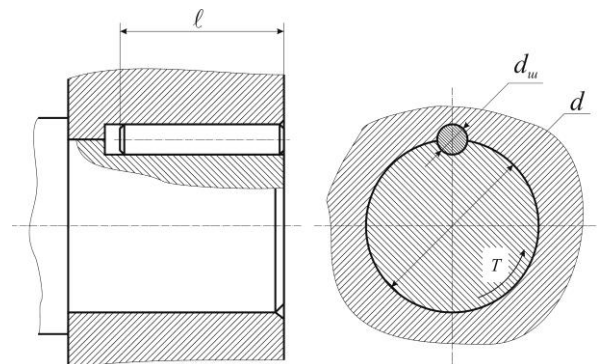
З'єднання деталей циліндричною шпонкою
